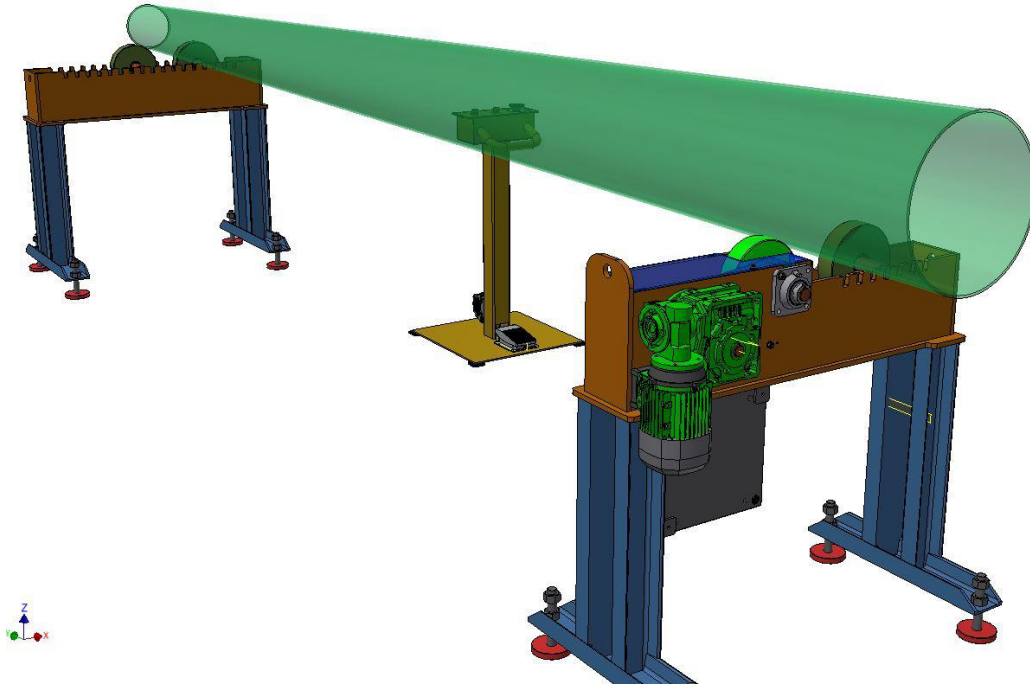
Welding turning supports - Projeto Steelpro.
